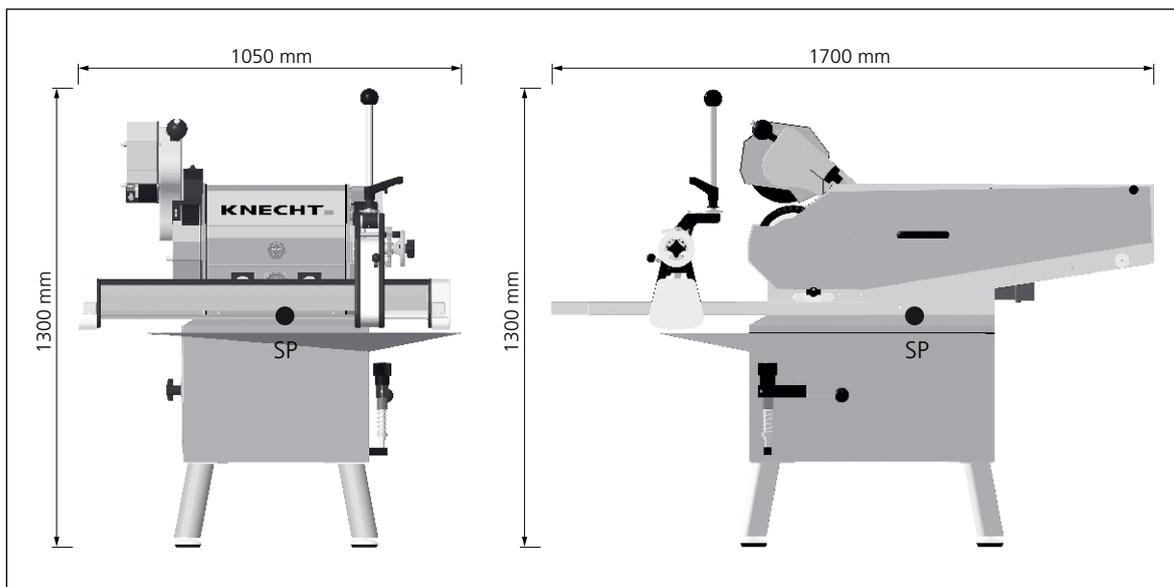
Dimensions S20 B en mm et centres de gravité (SP) de la machine
